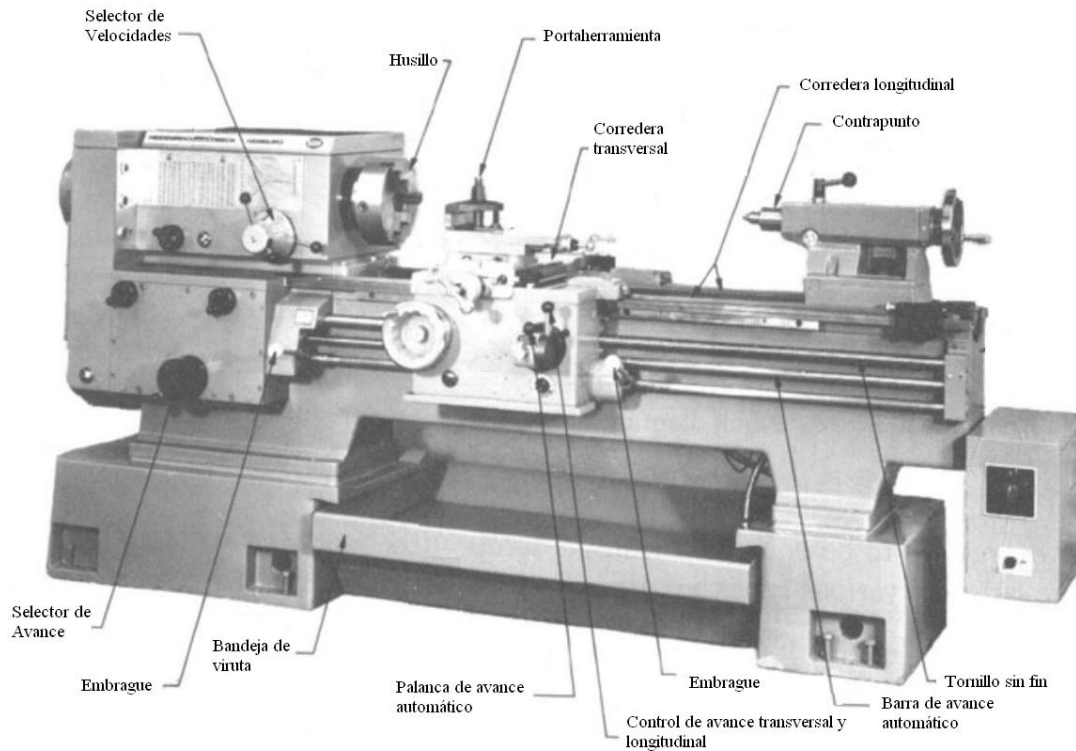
Torno tradicional (Fuente: [www.mec-tools.com](http://www.mec-tools.com))
